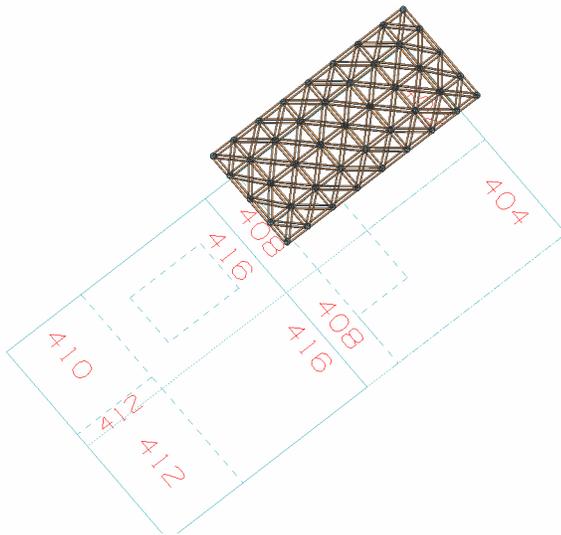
Raummodule mit Stützstrukturen des Deckhauses
